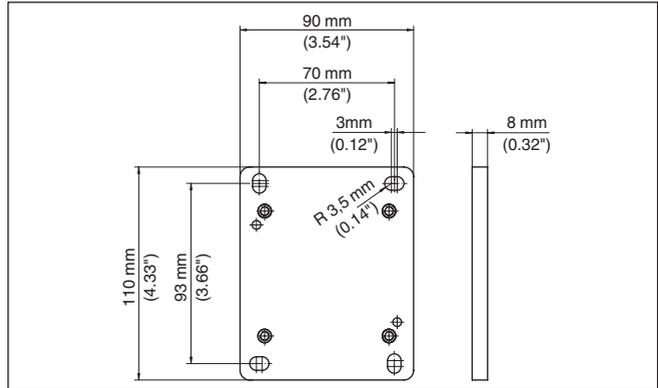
Plantilla de taladros - montaje mural (carcasa externa)
